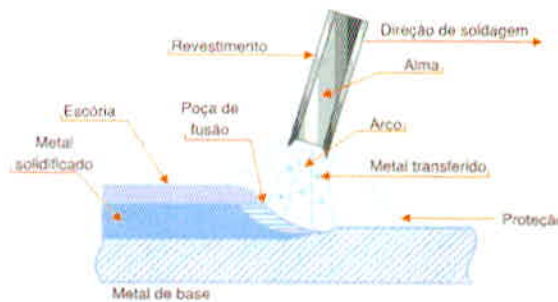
Detalhes da soldagem com eletrodo revestido.
